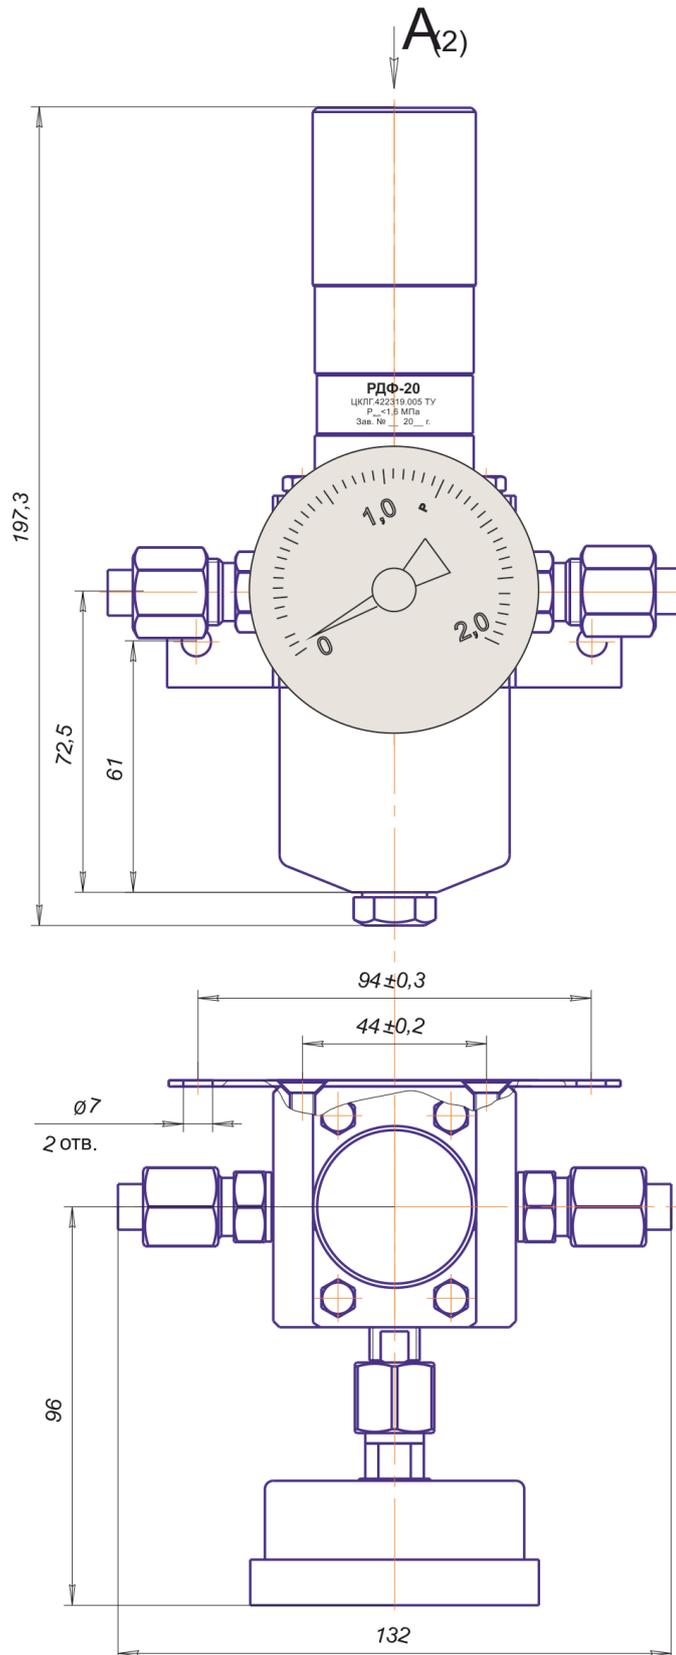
Габаритные и присоединительные размеры редуктора РДФ-20
